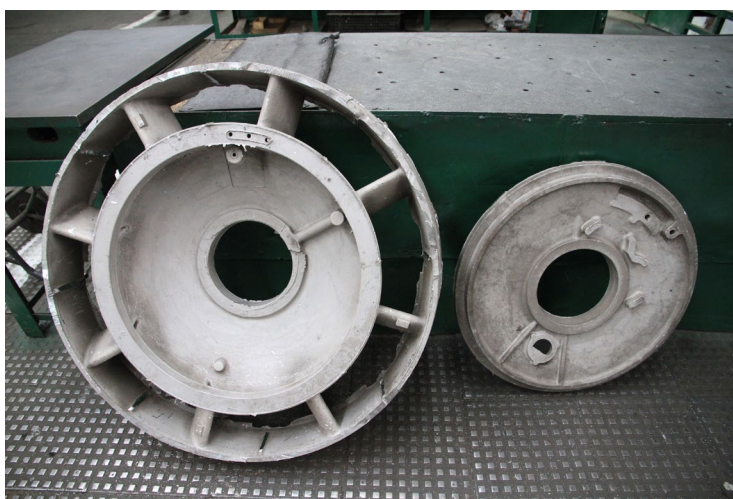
Отливки «Корпус промежуточной опоры» «Крышка промежуточной опоры» из сплава МЛ19 после выбивки и обрезки литниково-питающей системы (ЛПС)
